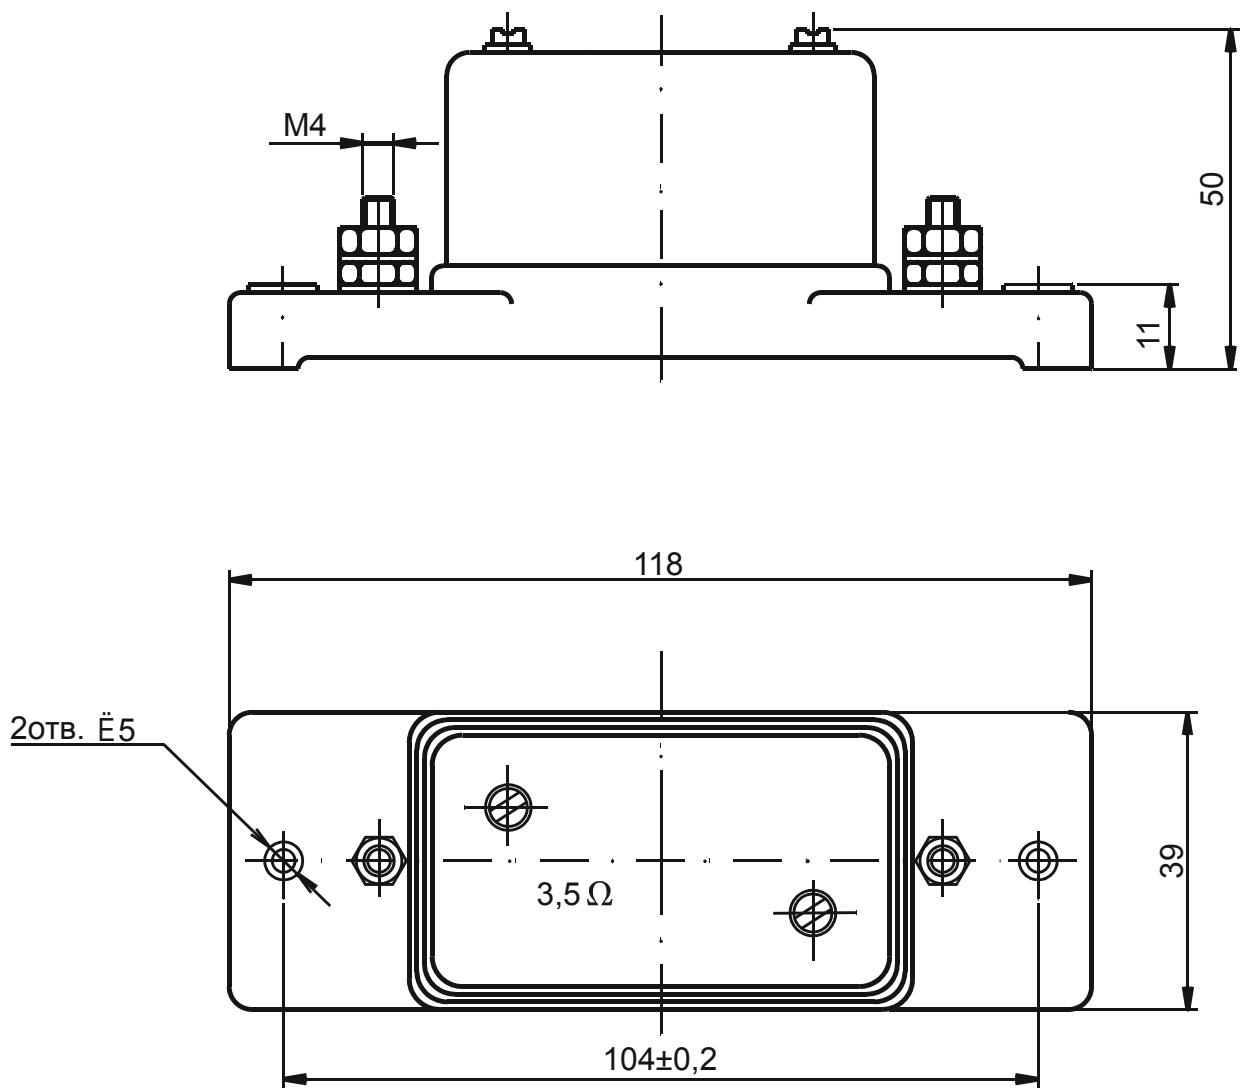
Габаритный чертеж резистора подгоночного Р1830
